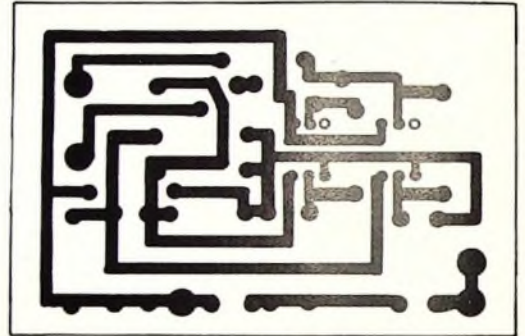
Printplatte für die elektronische Batterie-Ladezustandskontrolle (Maßstab 1:1)
